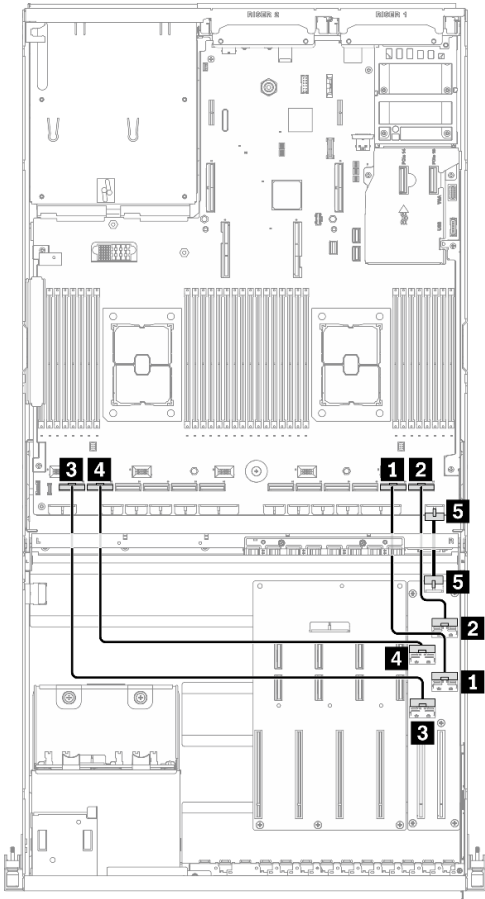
앞면 I/O 확장 보드 케이블 배선 - 구성 C
